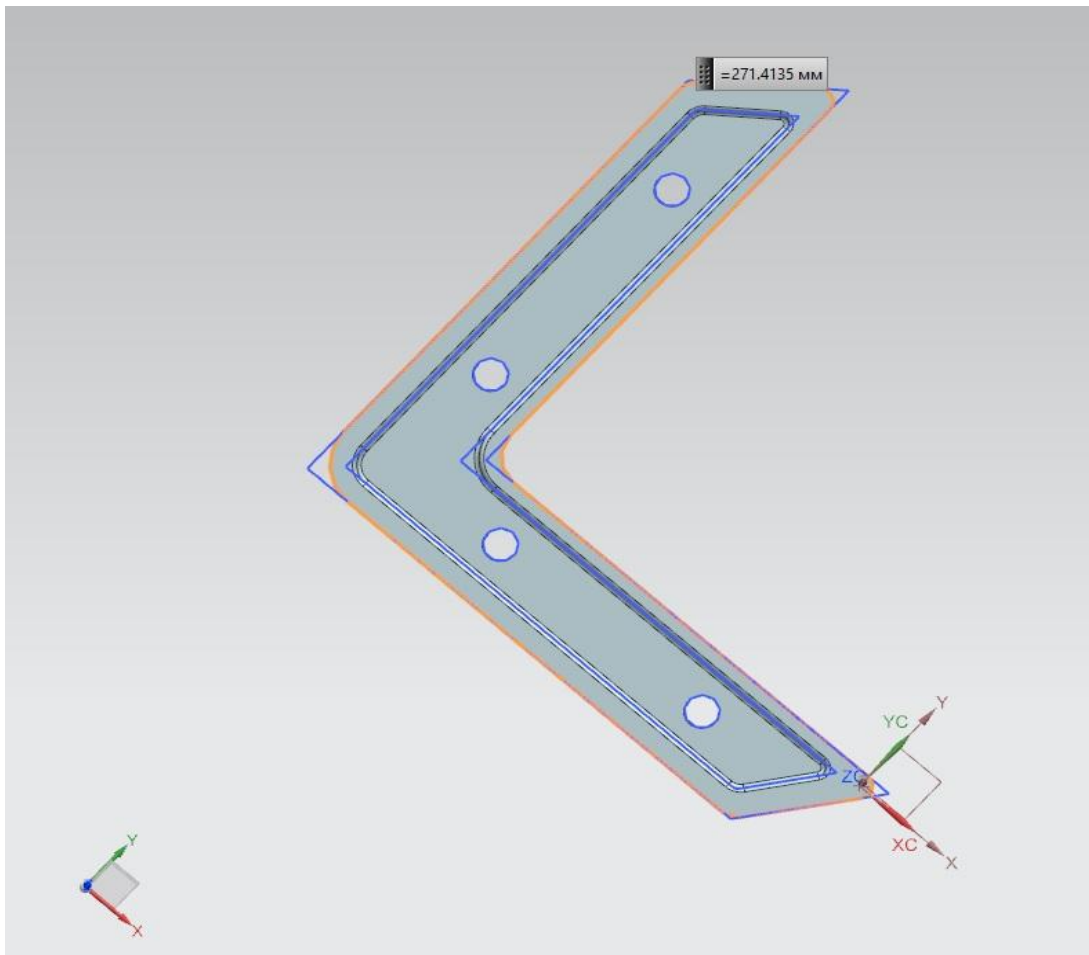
Длина линии реза предлагаемой заготовки
